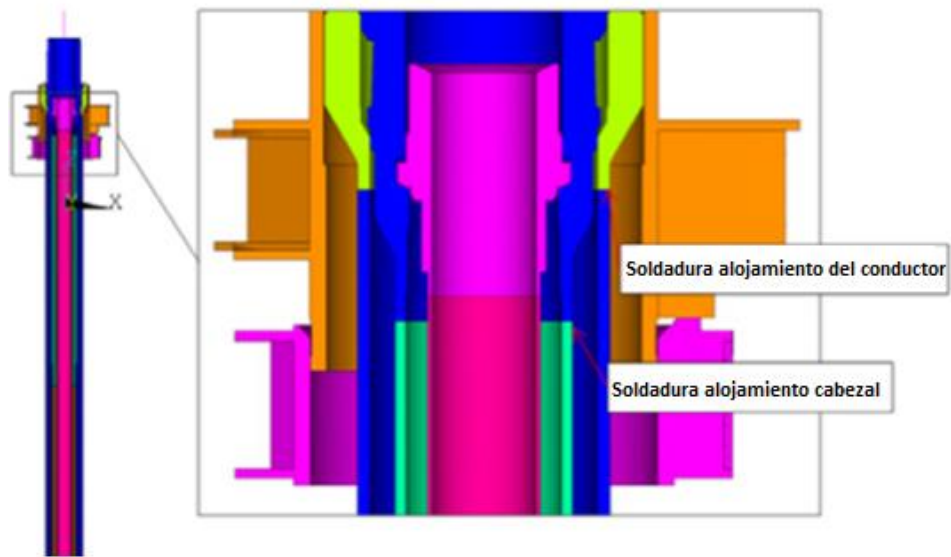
Soldadura de alojamientos de tuberías. Fuente: Wellhead Fatigue Analysis por Lorents Reinas (modificada por el autor).
